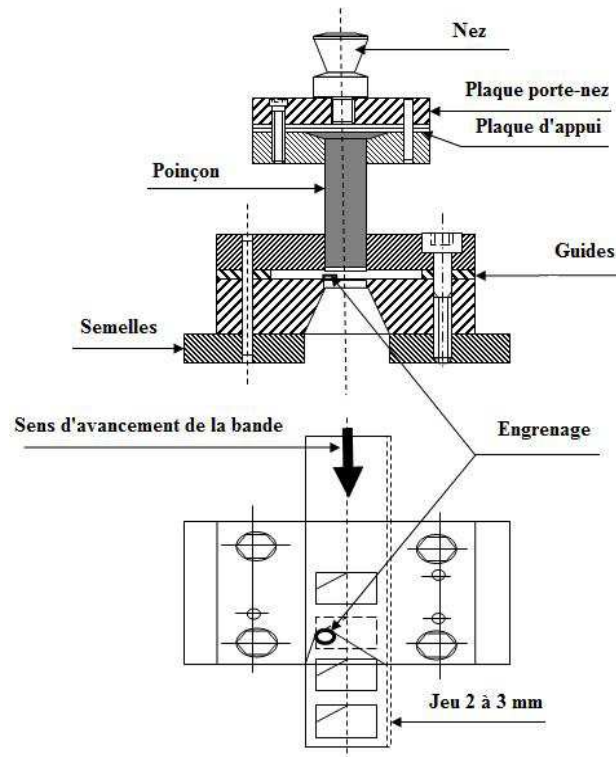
Outil à contre-plaque muni d'un avancement du flan par engrenage
